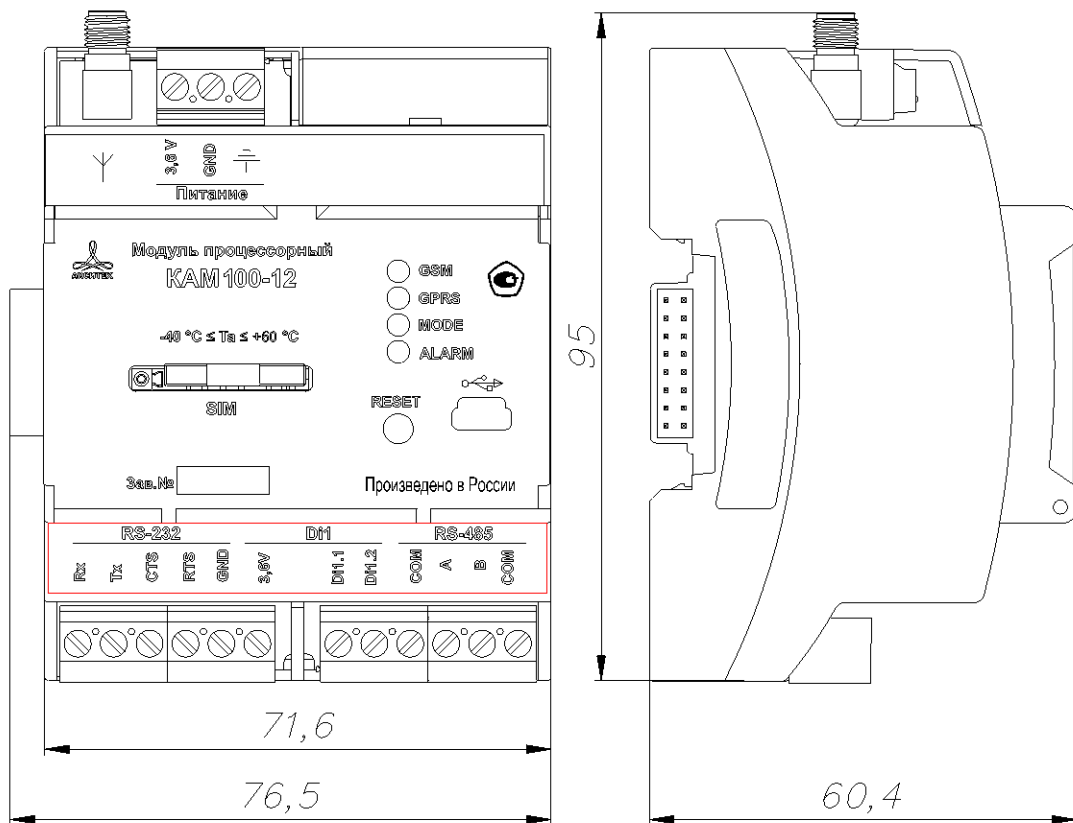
Внешний вид и габаритные размеры модуля процессорного КАМ100-12
